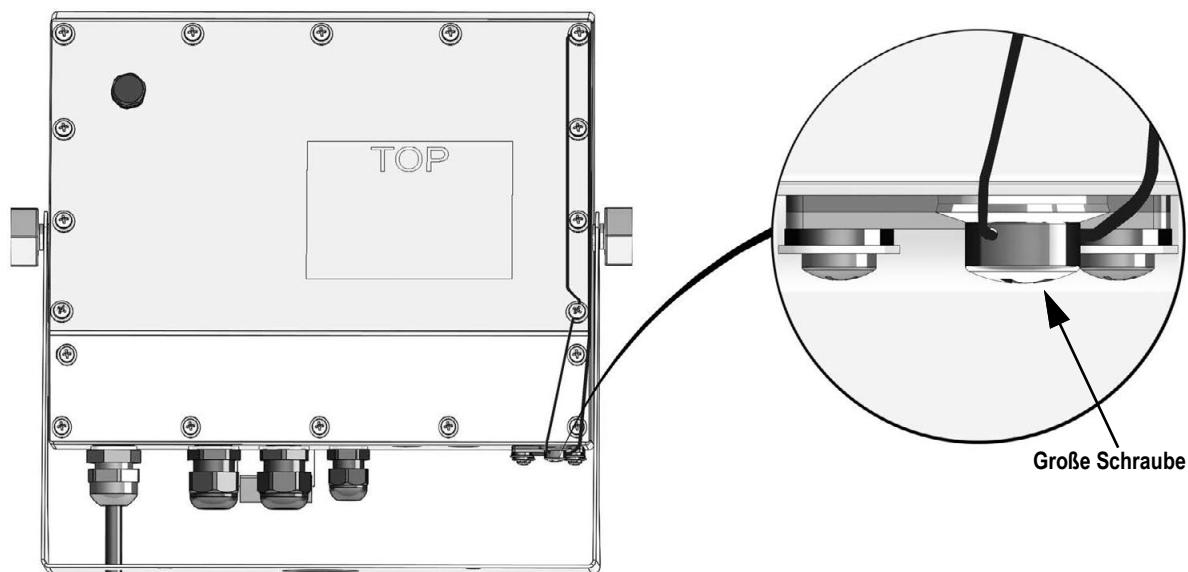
Versiegelung einer Gewichtsanzeige für die Universal-Montagehalterung
